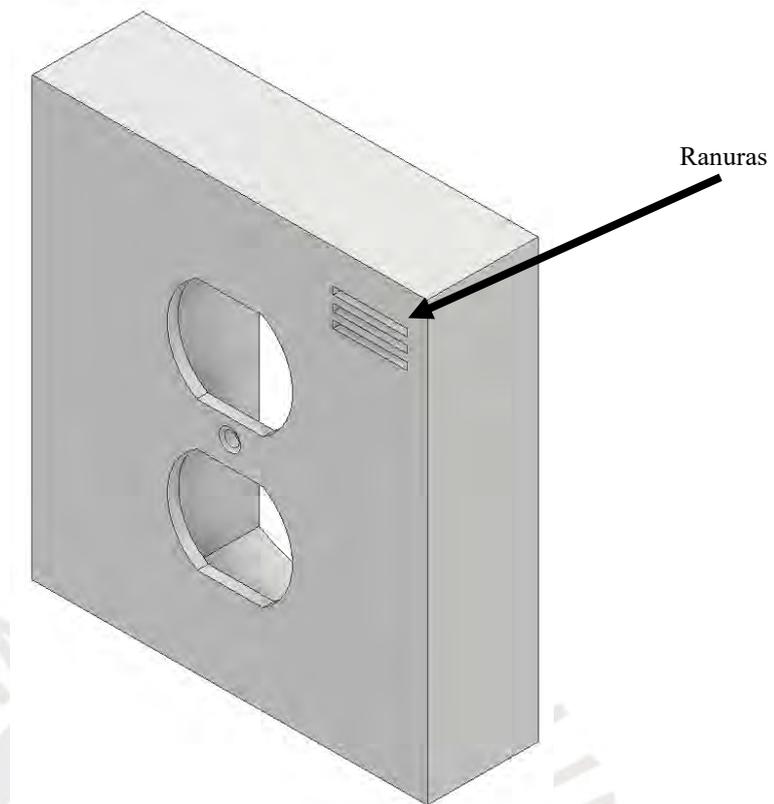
Diseño mecánico del dispositivo para tomacorrientes - frontal. Fuente: [21]
